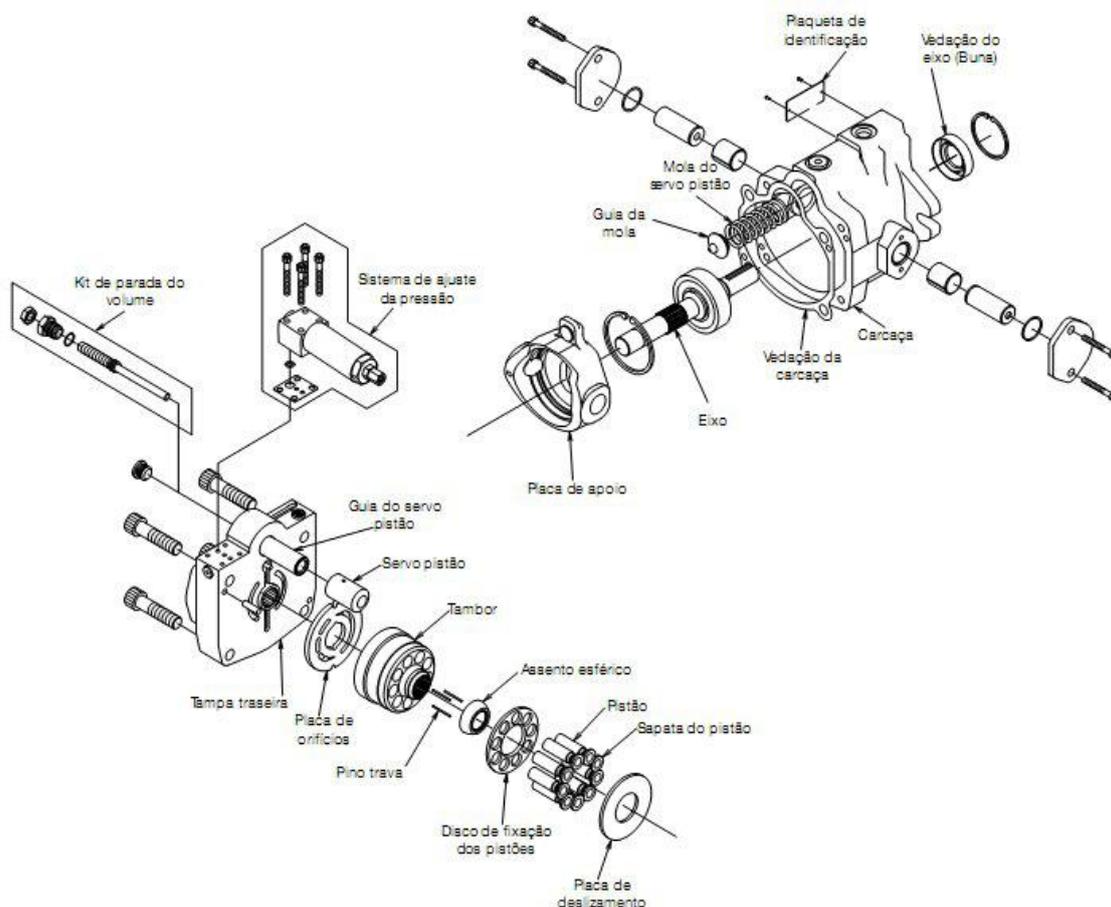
Desenho de Montagem – Bomba de Pistões Rotativos
